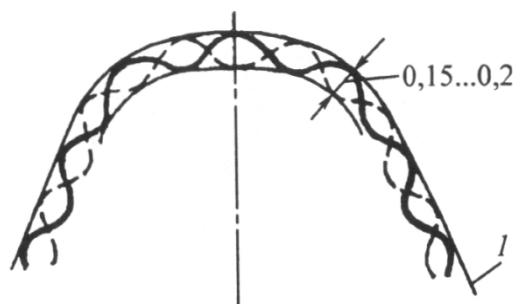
Прогрессивная схема резания с волнистым профилем зуба
